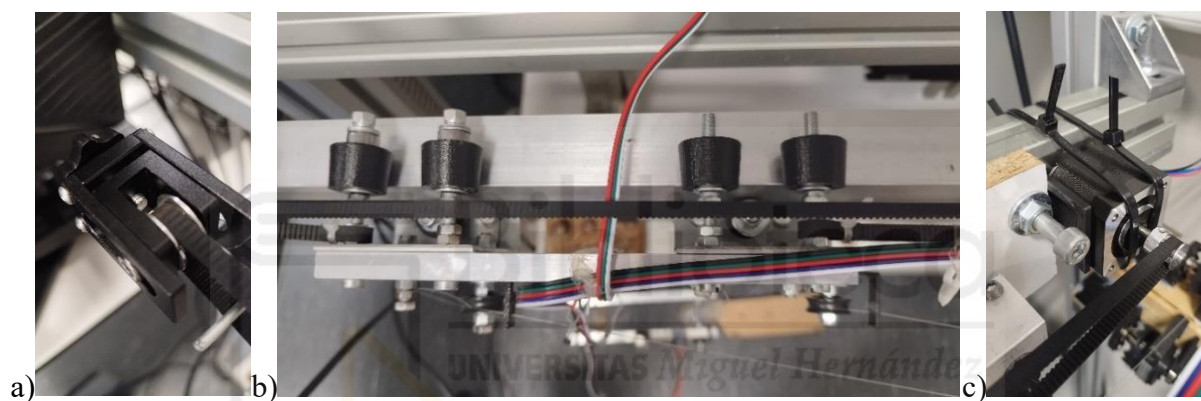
Transmisión del carro portador con la correa GT2: a) Polea dentada auxiliar ubicada en el extremo izquierdo, b) Anclaje de la correa GT2 al carro portador, c) Unión con el acople GT2 del motor horizontal.
